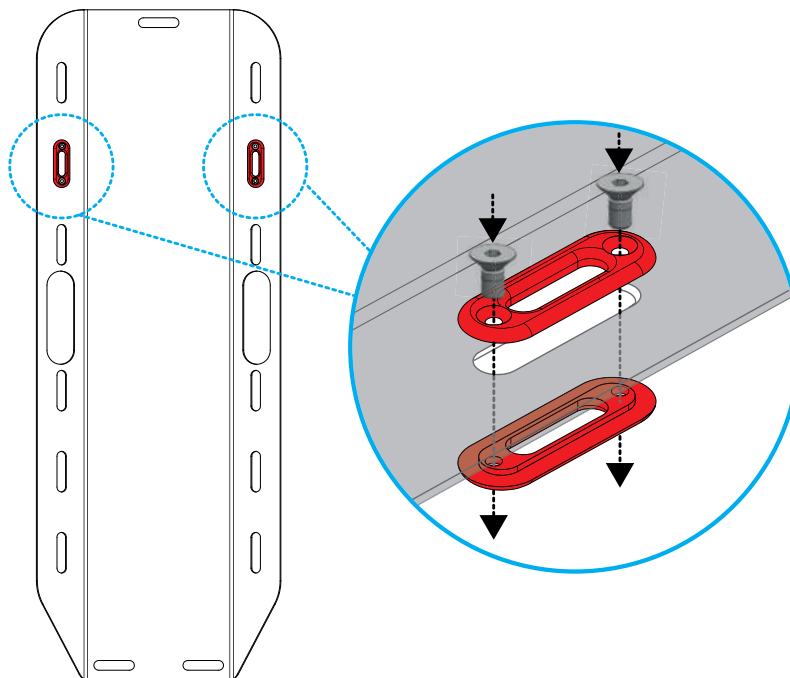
Assemblage des fentes de renforcement du KIT PRO
